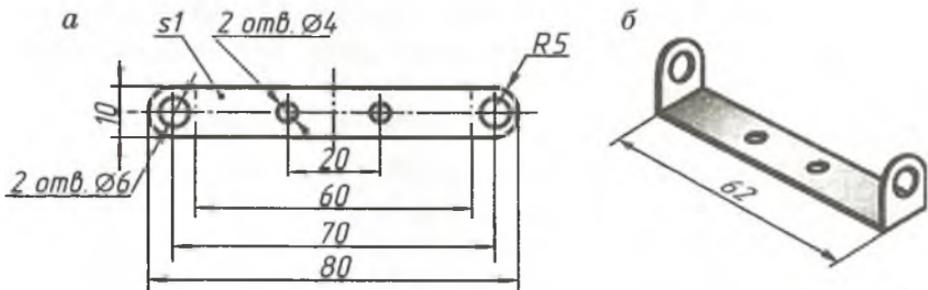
Чертеж развертки (а) и технический рисунок (б) скобы крепления оси
